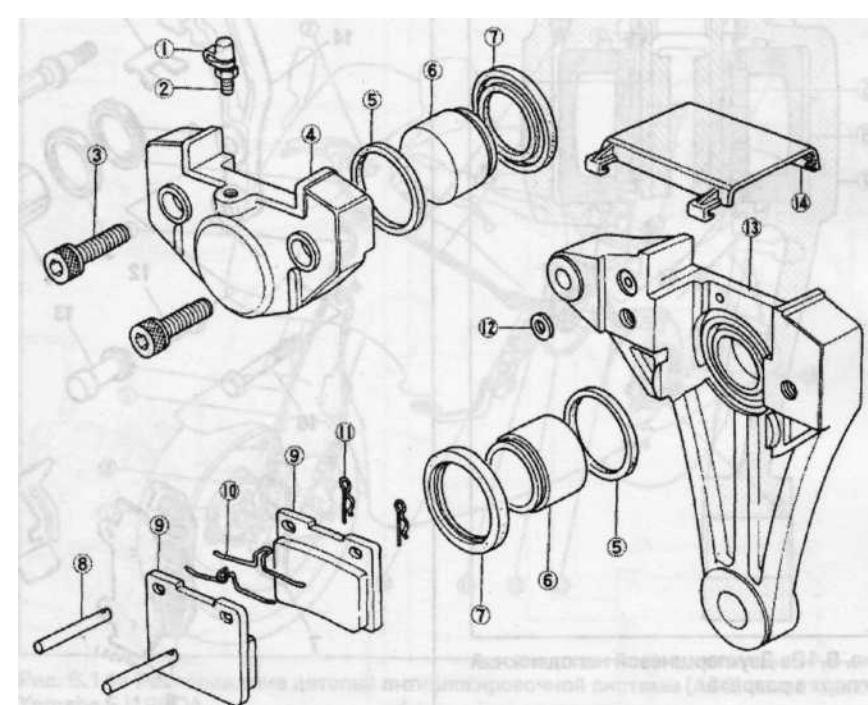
Типичный задний двухпоршневой неподвижный суппорт
